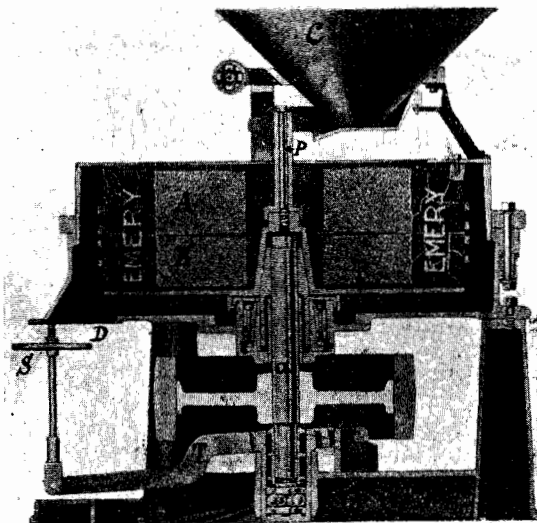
Młyn pionowy Sturtevanta (przekrój) M — sprzęgło cierne.
